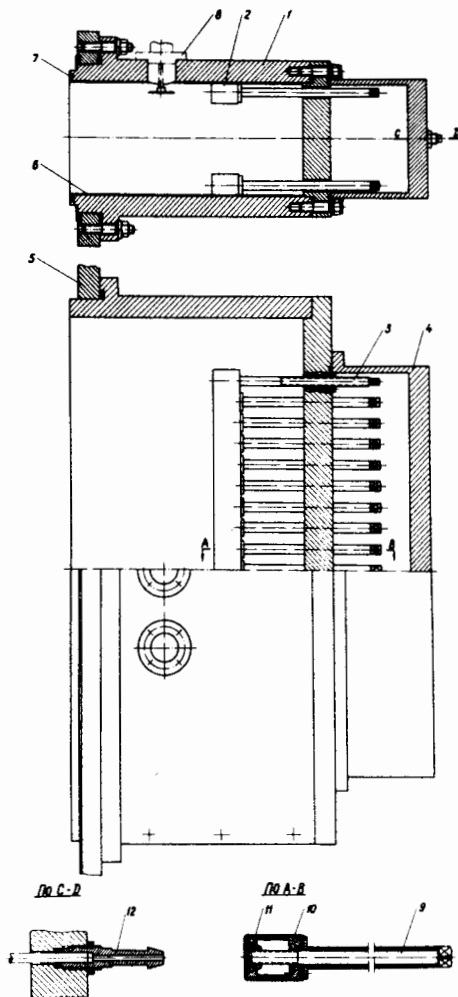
Резонансная линия. 1 - корпус резонансной линии, 2,9,10,11 - закорачивающее устройство, 3 - винт для перестановки устройства, 4 - кюмал, 5 - фланец, 6 - плакировка, 7 - резиновый шнур, прижимающий плакировку резонансной линии к плакировке камеры, 8 - датчик высокочастотного напряжения, 12 - оливка для подвода воды.
